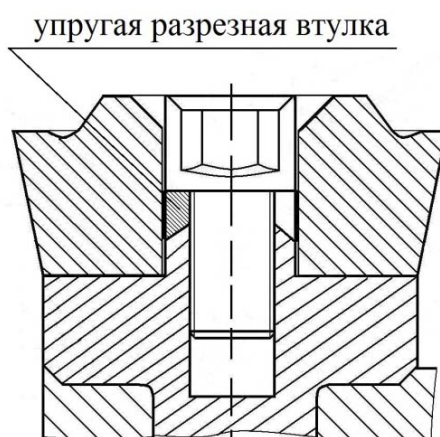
Усовершенствованная конструкция сборного чашечного резца
